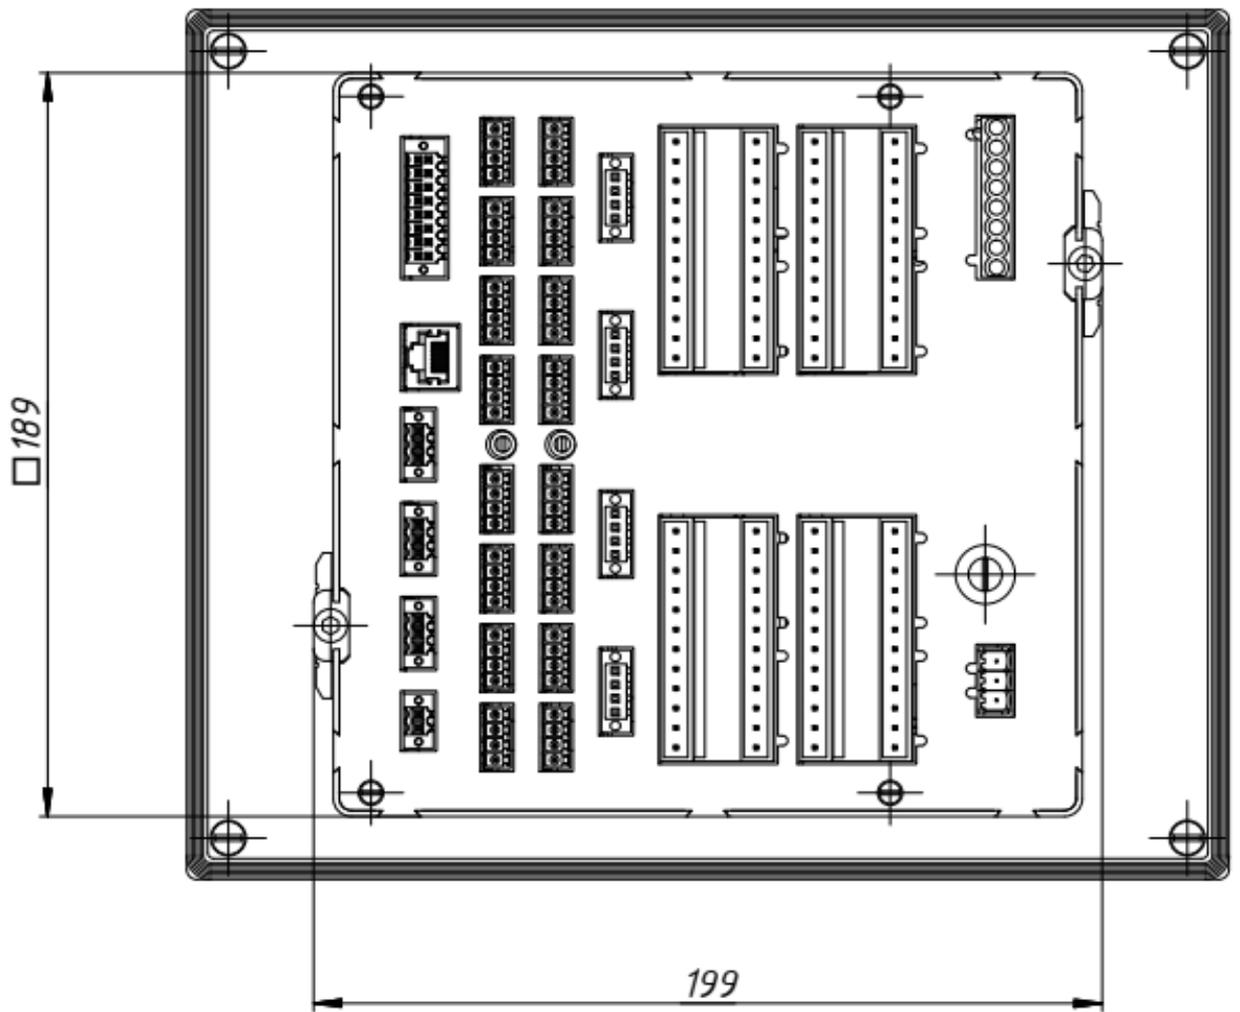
Габаритный чертёж прибора в исполнении Ф1772-1, вид сзади
